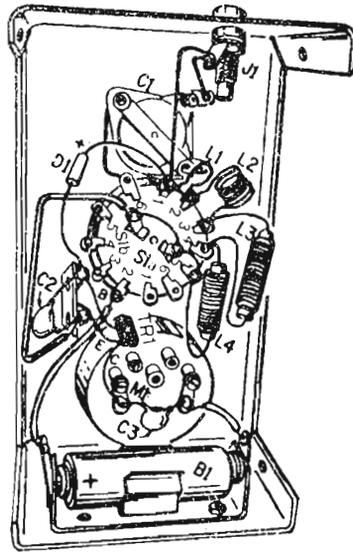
Schema pratico di montaggio del rivelatore di trasmettenti.
